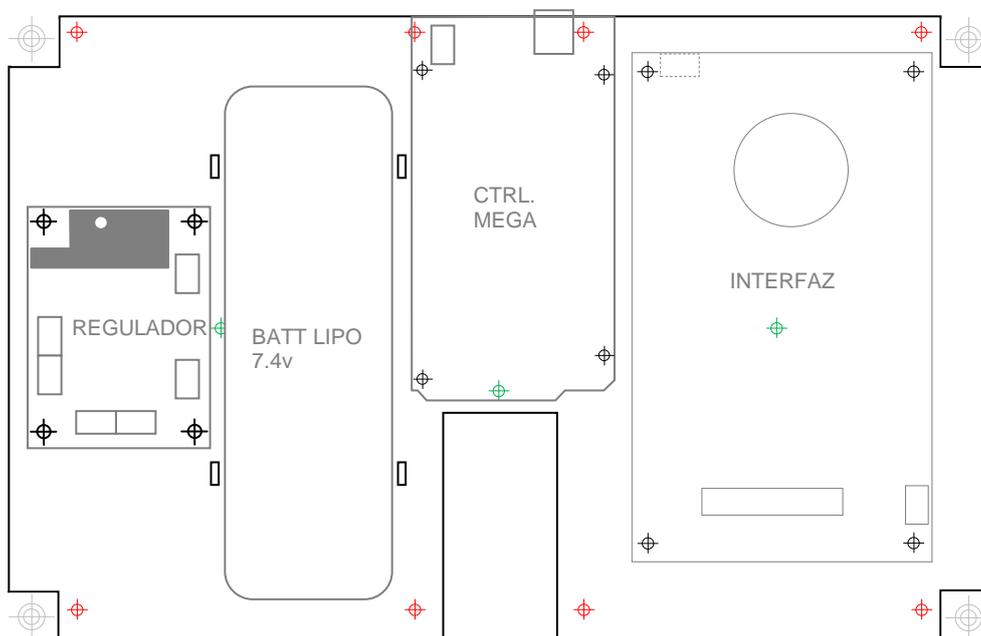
Vista en planta de la placa de base para la electrónica. Todos los orificios son de 3 mm.
